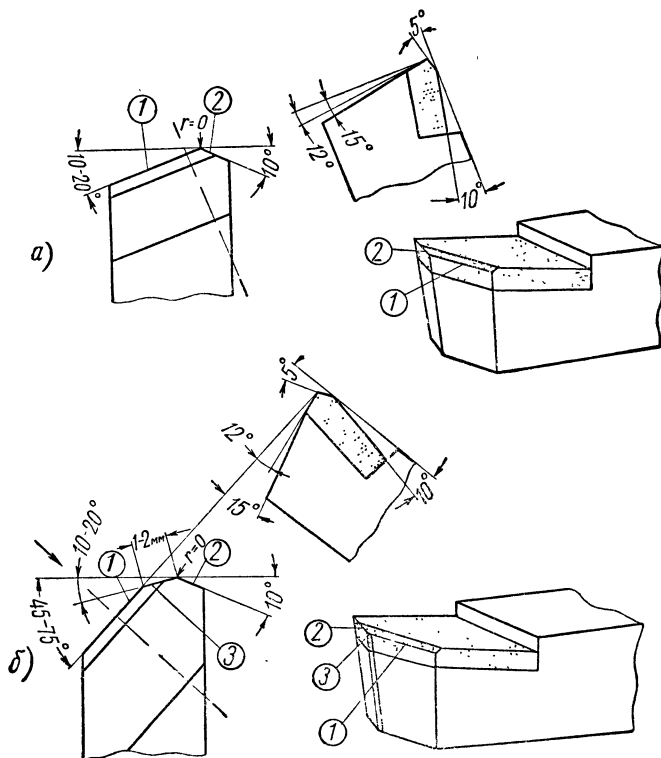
Проходной резец для чистовой обработки стали конструкции лауреата Сталинской премии Н. Ф. Подвезько.
